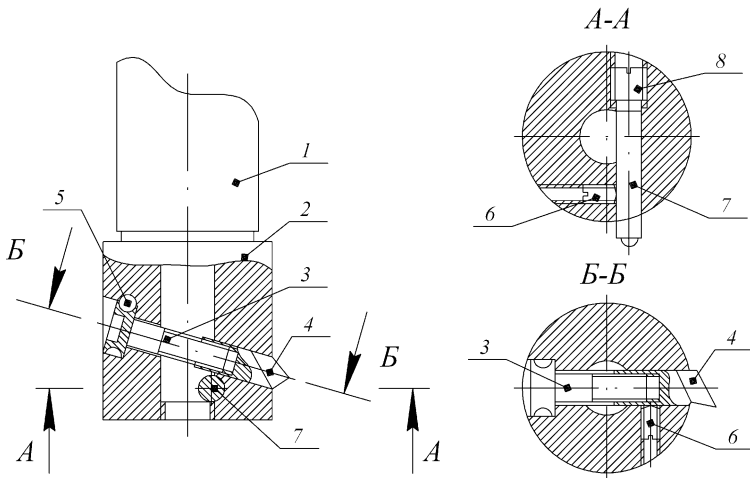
Шпиндель станка 278Н: 1 – шпиндель; 2 – резцовая головка; 3 – регулировочный винт выхода реза; 4 – резец; 5 – штифт; 6 – зажимной винт; 7 – шариковая оправка; 8 – регулировочный винт шариковой оправки
